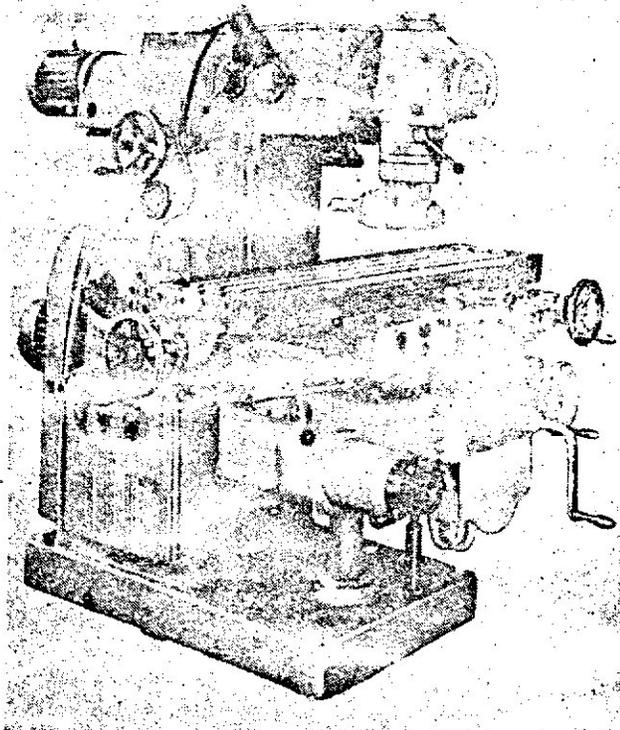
Широкоуниверсальный консольно-фрезерный станок модели 6М82Ш
